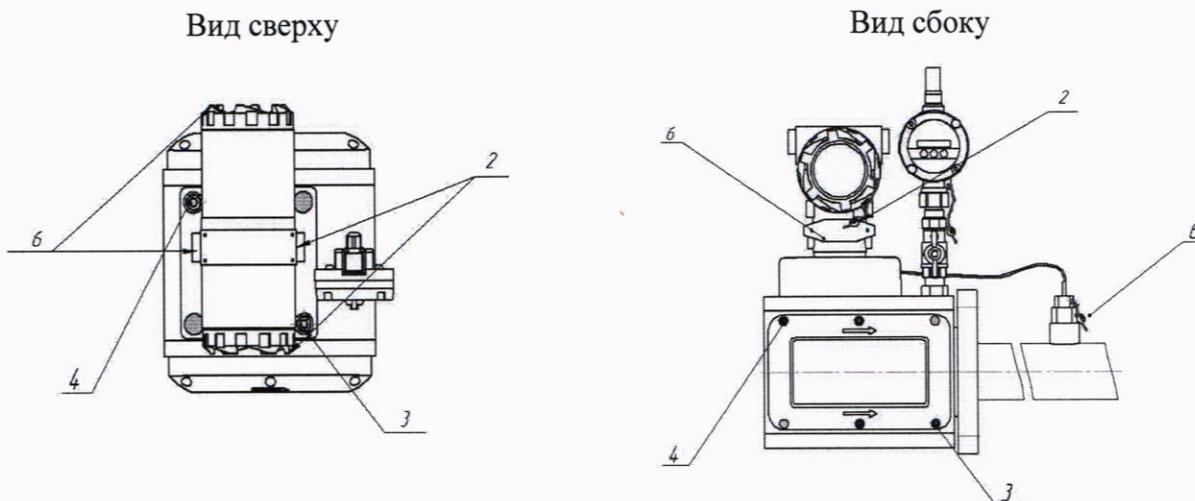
Корпус прямоугольного сечения с совмещенными защитными крышками
